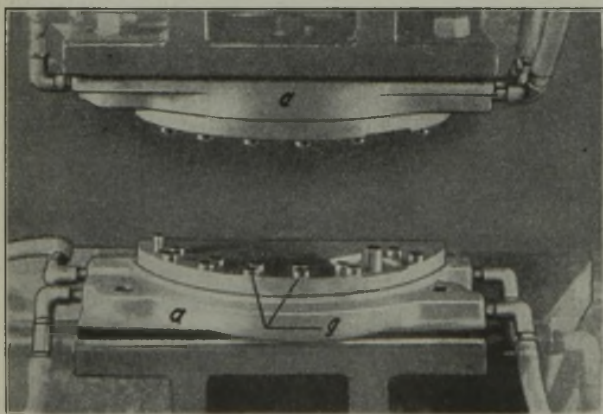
Sonderwerkzeug und Elektrode für die Projektionspunktschweißung.
